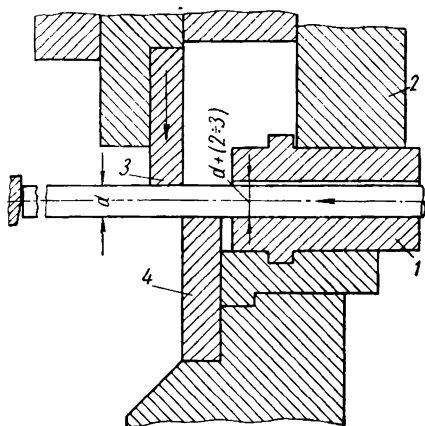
Схема резки проката диаметром до 70 мм с уравновешивающей направляющей втулкой: 1 — уравновешивающая втулка; 2 — прижим; 3 — верхний нож; 4 — нижний нож
